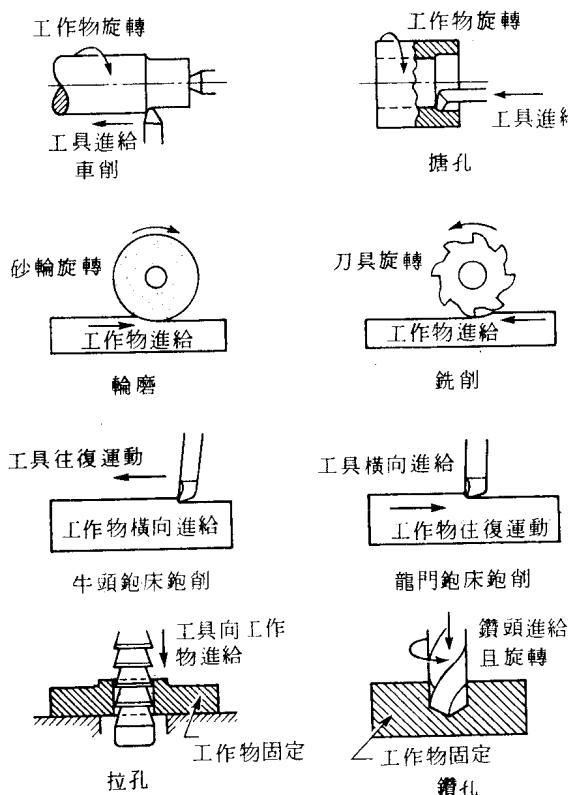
切削零件至特定尺寸之傳統加工方法。
